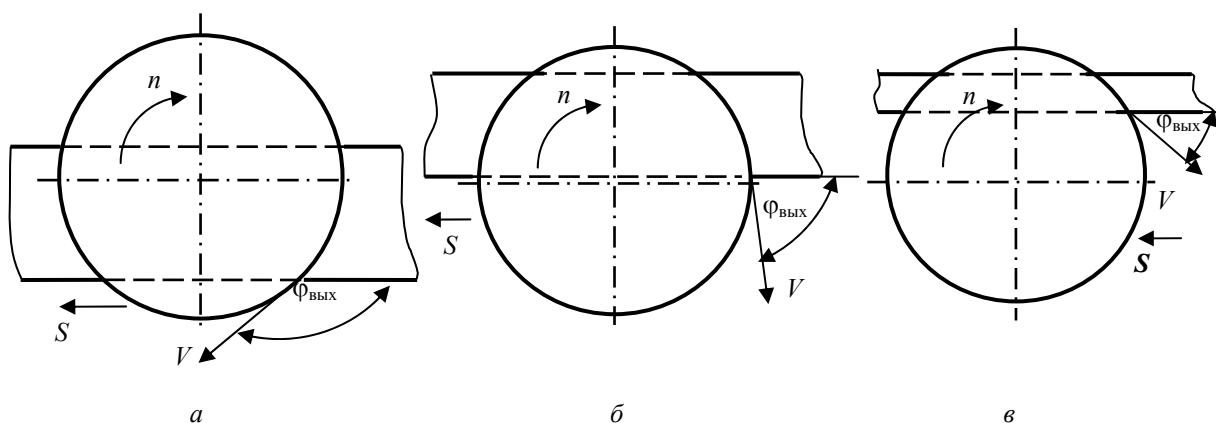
Схема расположения фрезы и заготовки при разных углах выхода:
